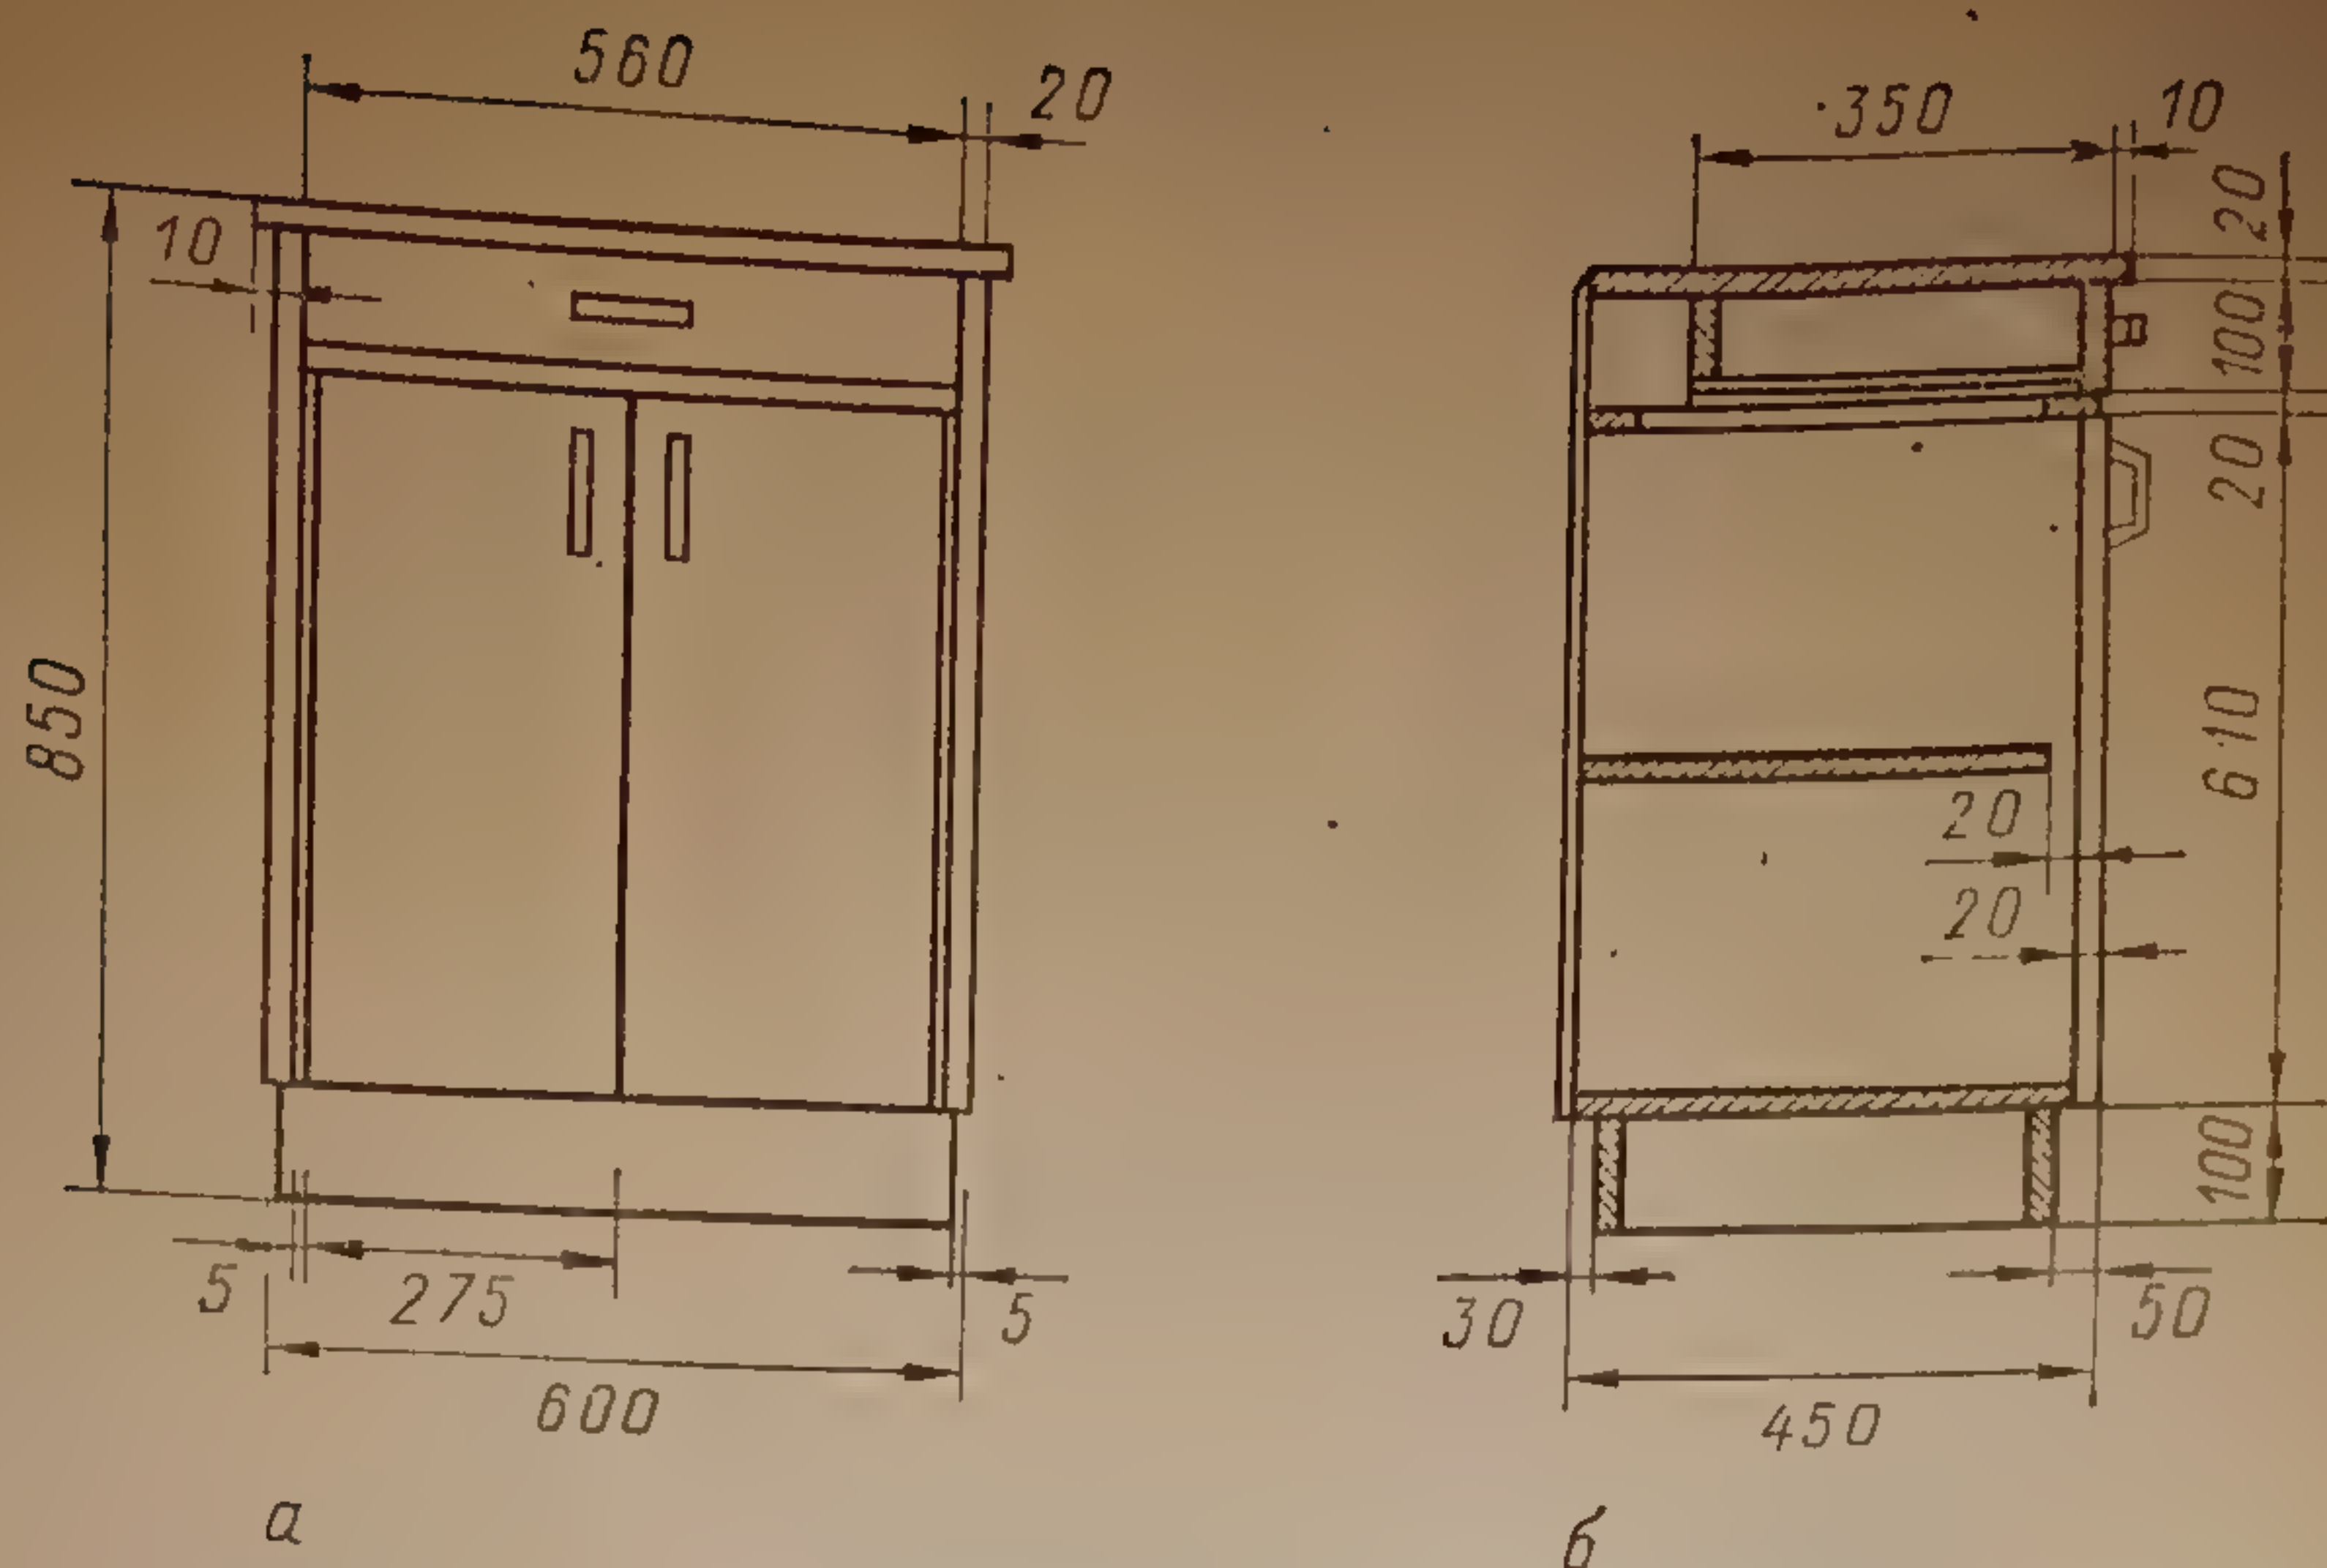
Эскиз разделочного стола-шкафа: а — вид спереди; б — поперечный разрез
